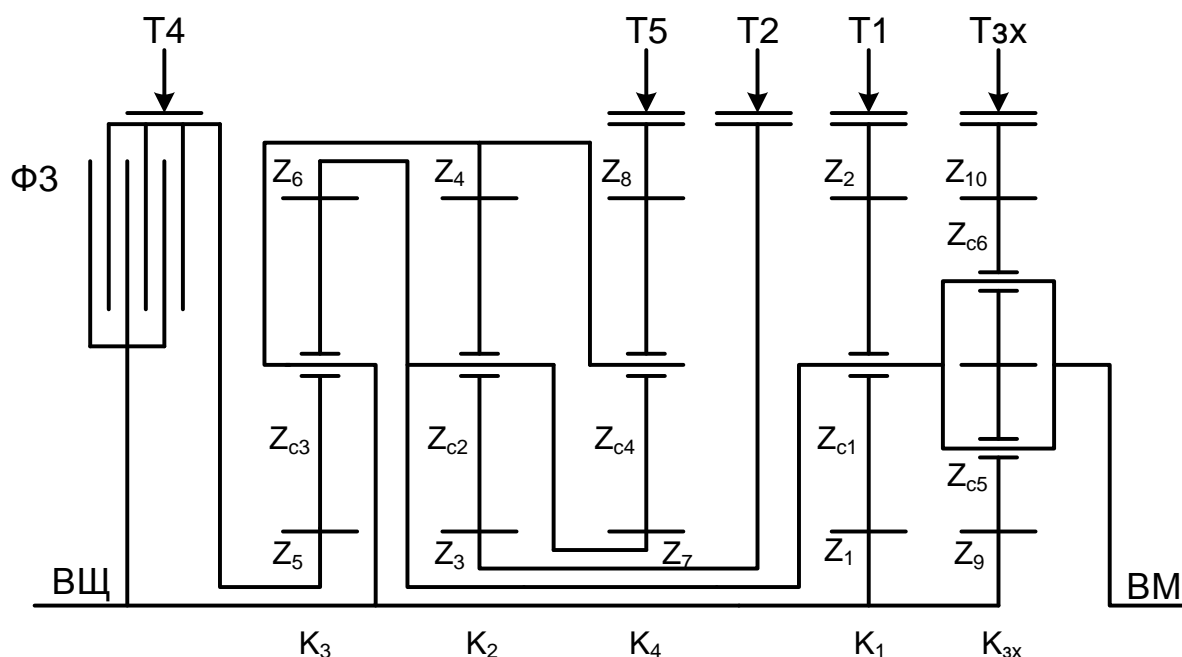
Схема бесконтурной коробки планетарных передач по типу 5+1 с двумя повышающими ступенями
